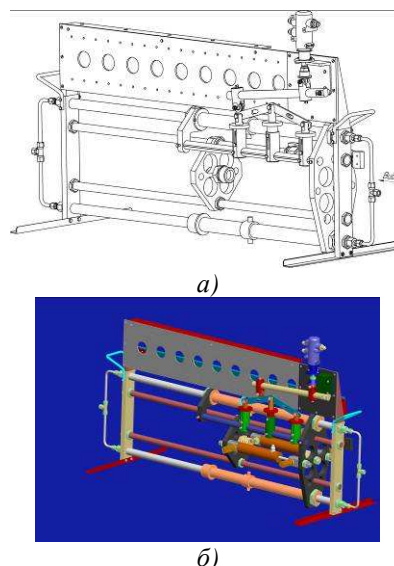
Креслення стенда для випробувань гідроциліндрів: а) загальний вид стенда; б) 3D-модель стенда
